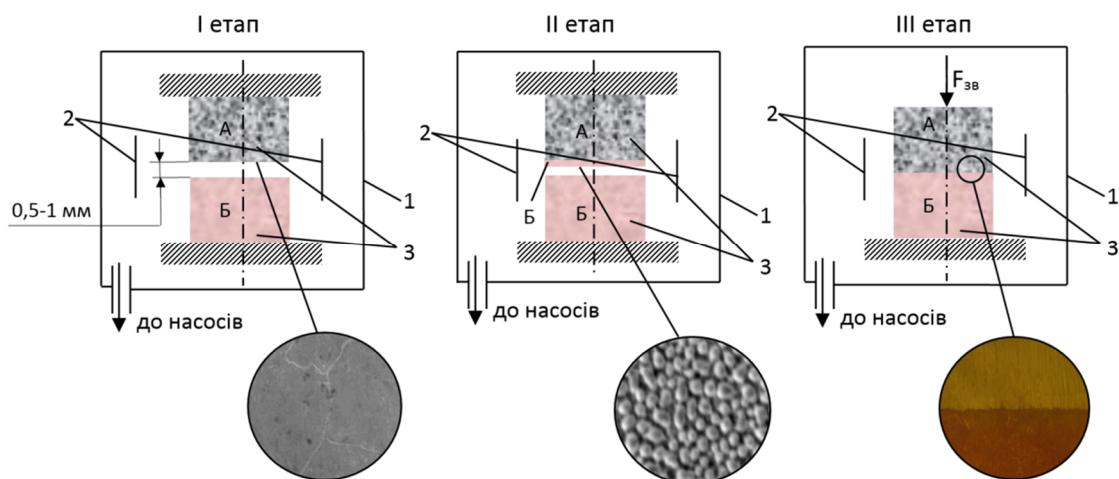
Стадії формування нероз'ємних з'єднань при зварюванні тиском у твердій фазі з використанням поверхневих фізико-хімічних процесів: 1 – вакуумна камера; 2 – нагрівач; 3 – деталі, що зварюються
